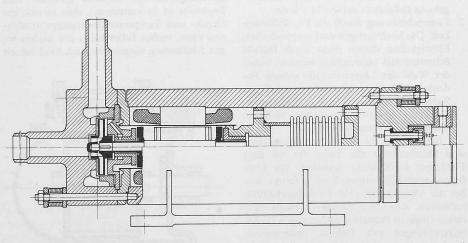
Pumpe mit Spaltrohrmotor für Drücke über 100 kp/cm² mit Druckausgleichskompensator und Oelfüllung im Statorraum des Elektromotors
